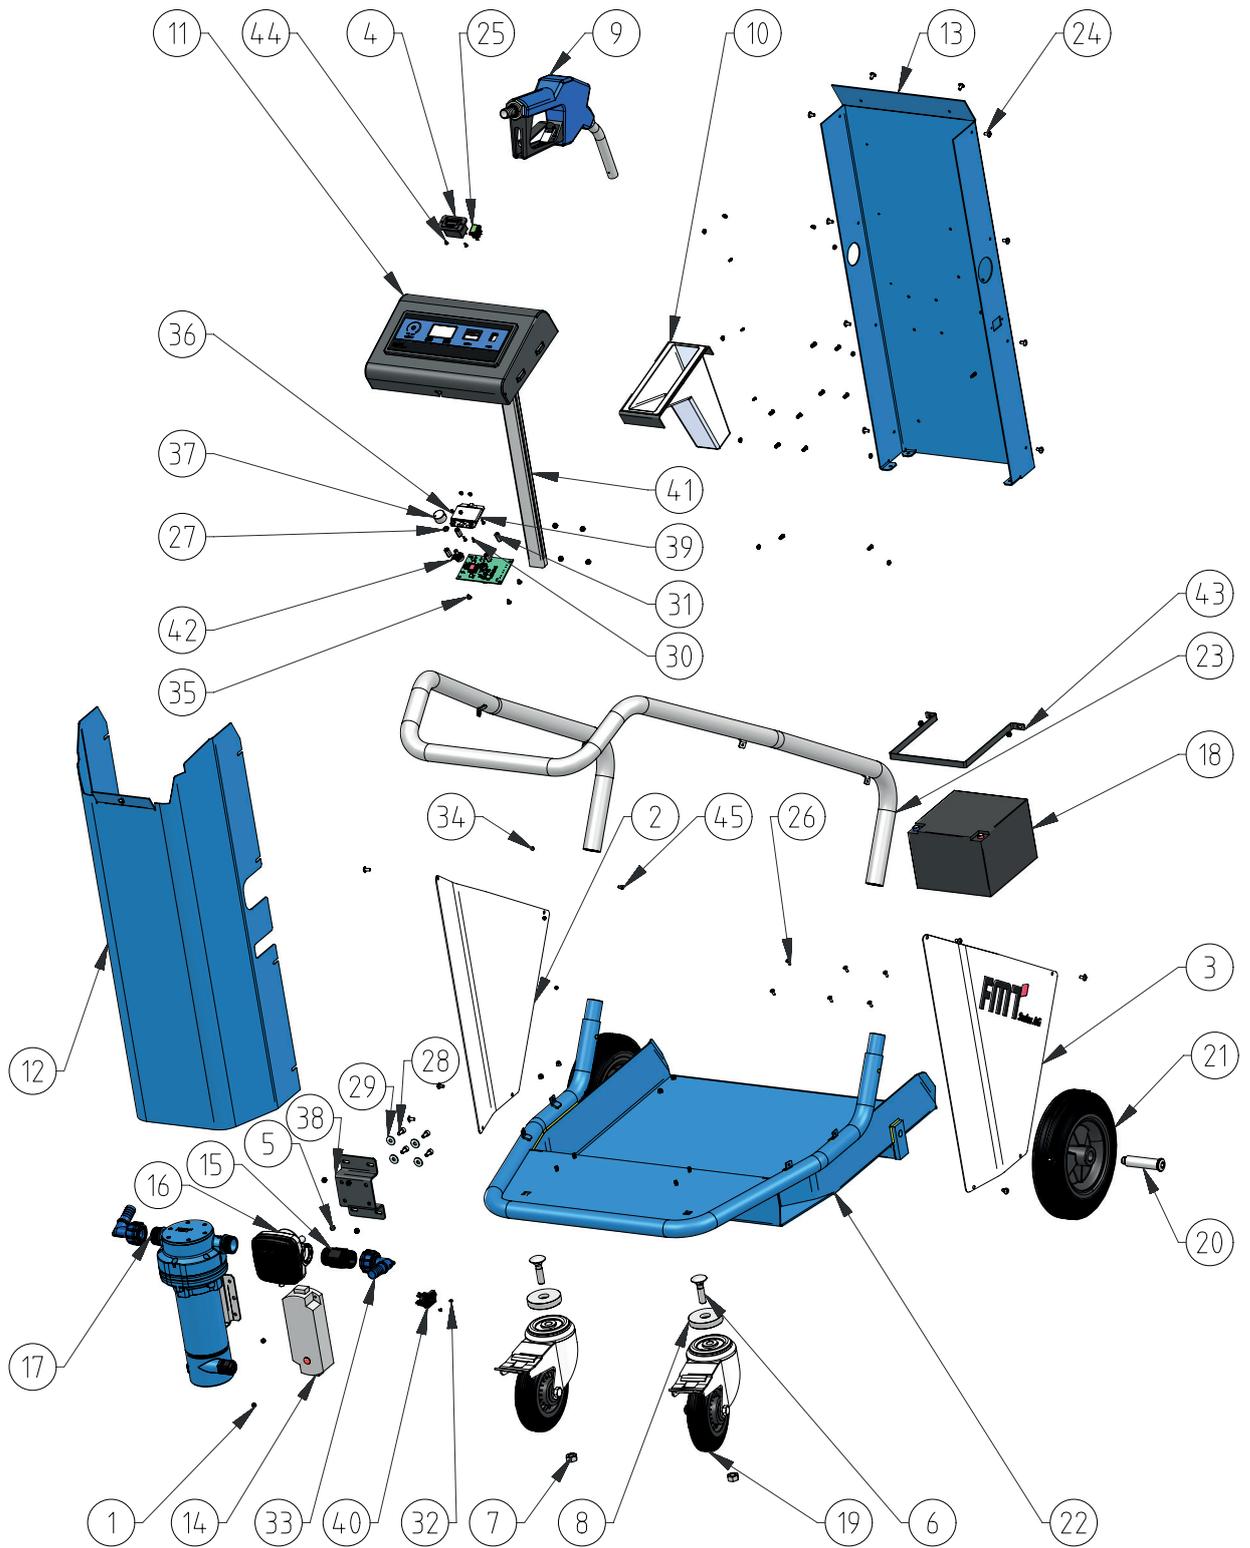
Vue éclatée mobiSERVE 200 I
